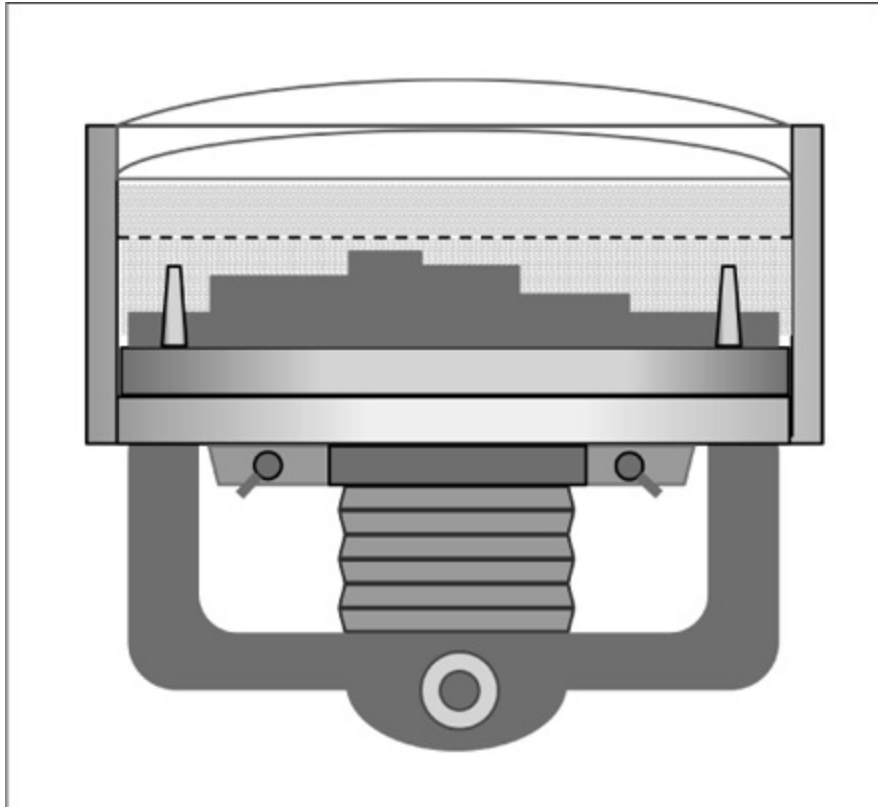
Máquina para la fabricación del molde. Elementos principales.
